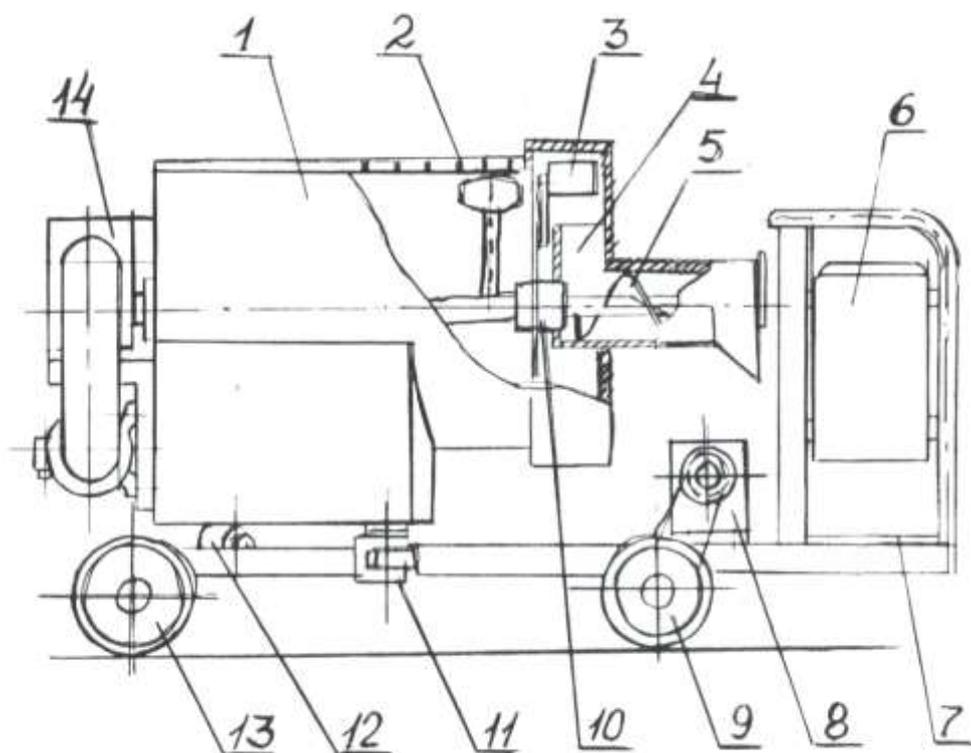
Схема устройства кормораздатчика с питателем ковшового типа:
